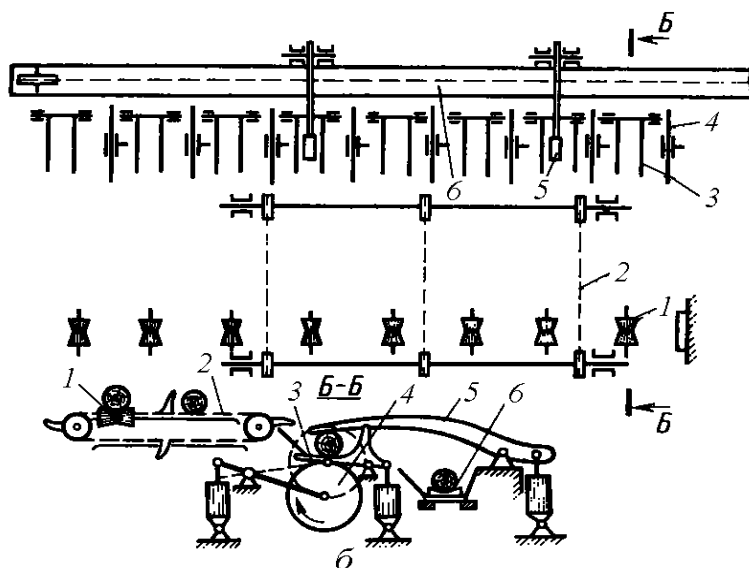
Раскряжевочные установки триммерного типа с поперечным перемещением хлыста: *а* – триммер с пилением движущегося хлыста; *б* – с пилением неподвижного хлыста
